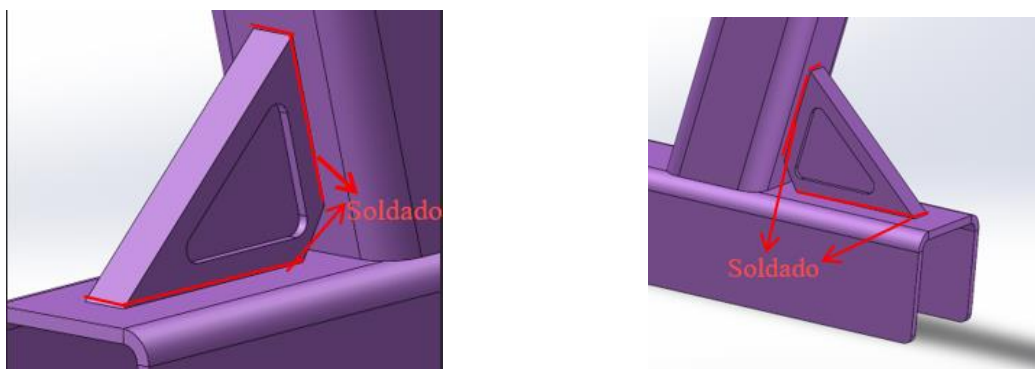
Vistas de soldado superior de pieza N°1 (Fuente 83)
